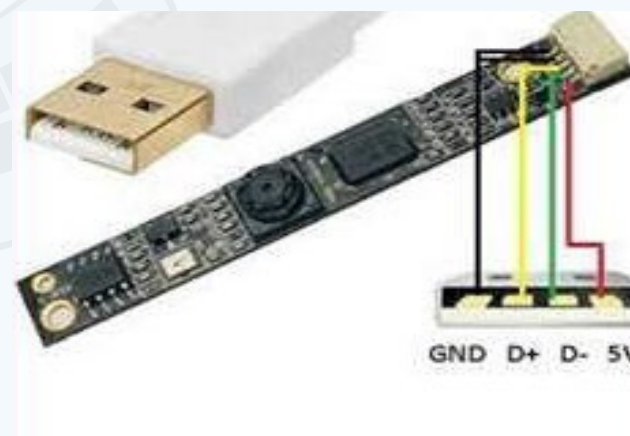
Soldadura del cable USB con el módulo de la cámara web
